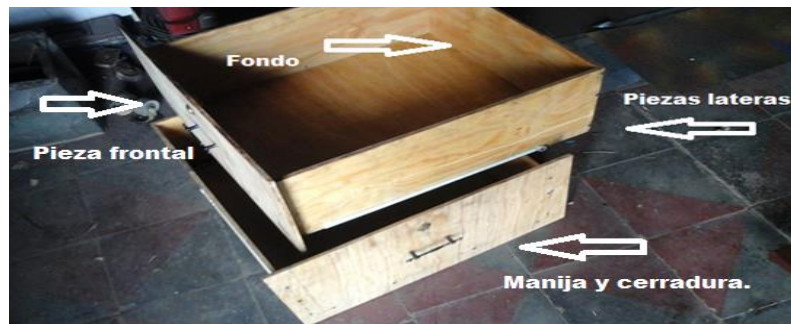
Corte de las piezas de plywood que formaran las gavetas (Fuente propia).
